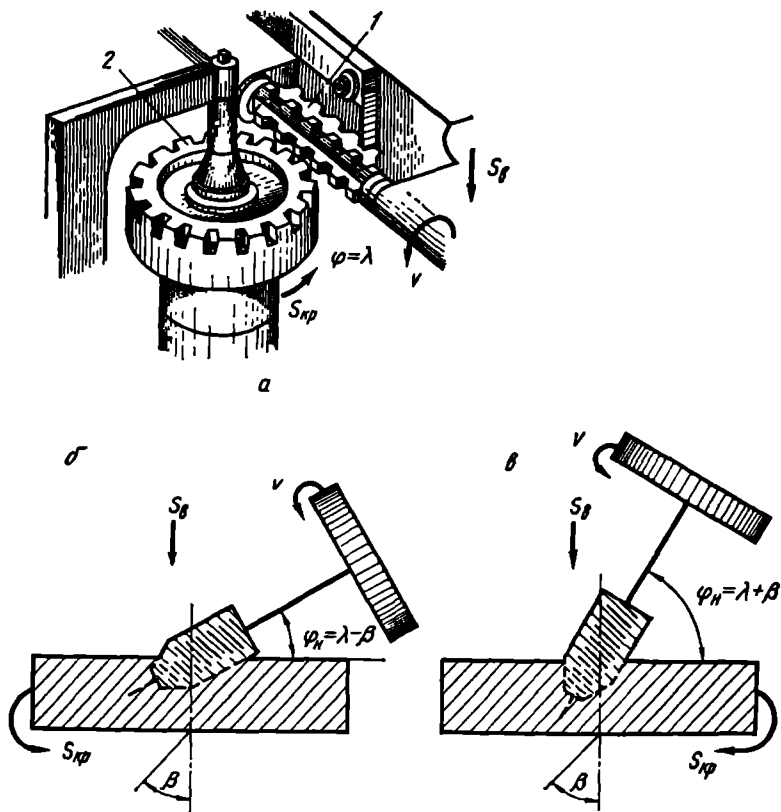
Схемы фрезерования зубьев по методу обкатки
